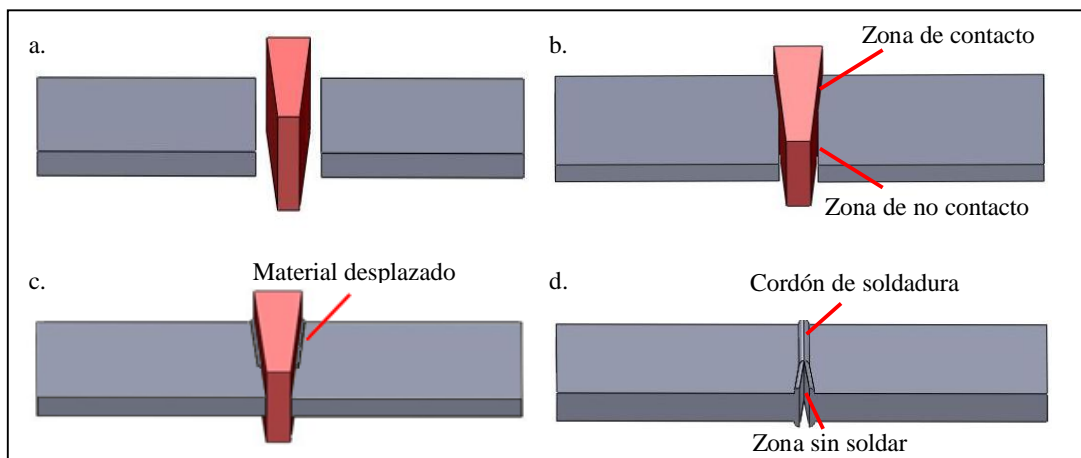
a- Momento inicial. b- Momento en que se ejerce presión en la pieza quedando zonas de contacto y zonas que no. c- Zonas con desplazamiento de material en momento de fusión del mismo. d- Soldadura no completa de la pieza.
